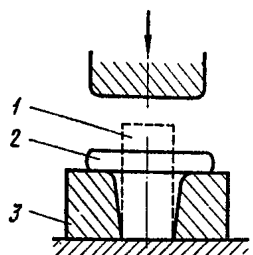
Осадка верхнего торца при концевой высадке под молотом: 1 — исходная заготовка, 2 — высаженная заготовка, 3 — кольцо
